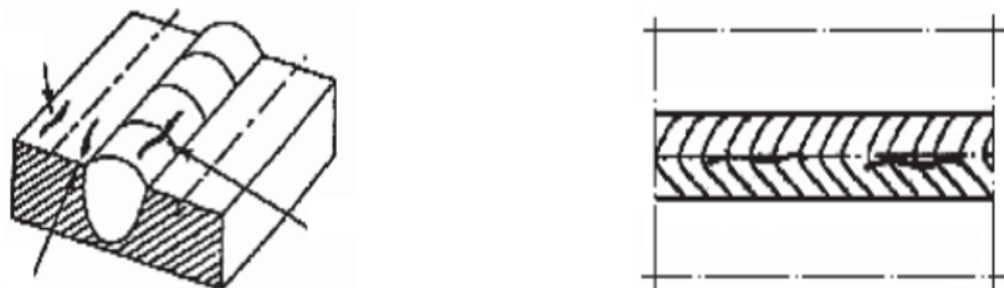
Эскиз дефекта сварного шва
